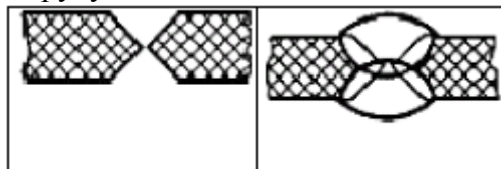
Схематичне зображення зварного з'єднання "С14"
